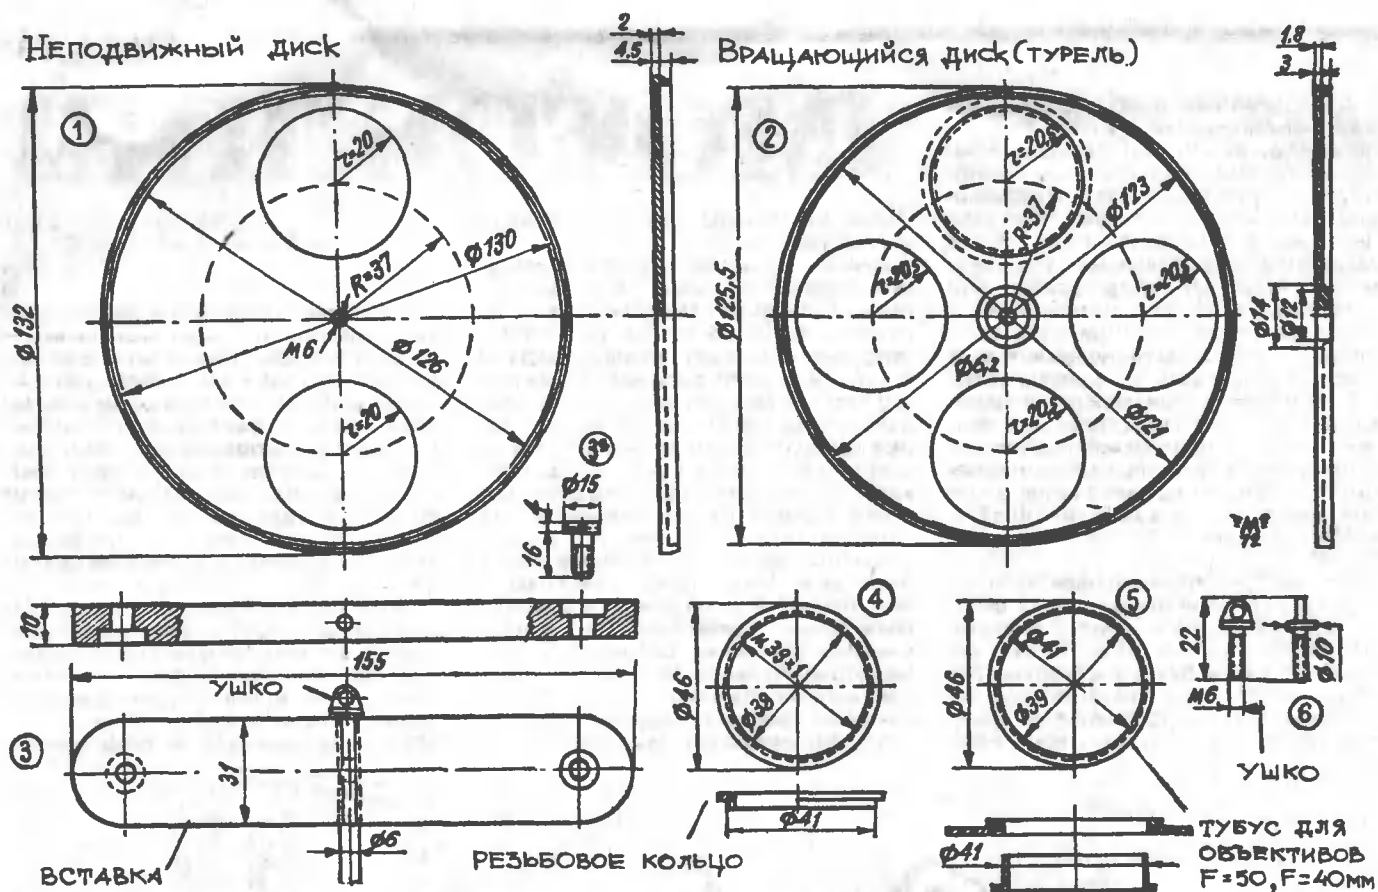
Габаритный чертеж турели и ее крепления к корпусам фотоаппаратов «Зенит»:
